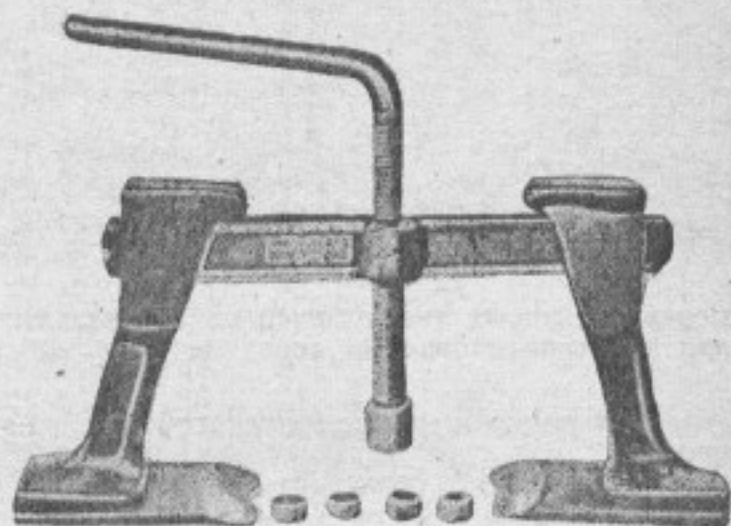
Ручной раздвигающийся с'емник фирмы Бош для работы с большими диаметрами (шкивы, зубчатки и пр.)
